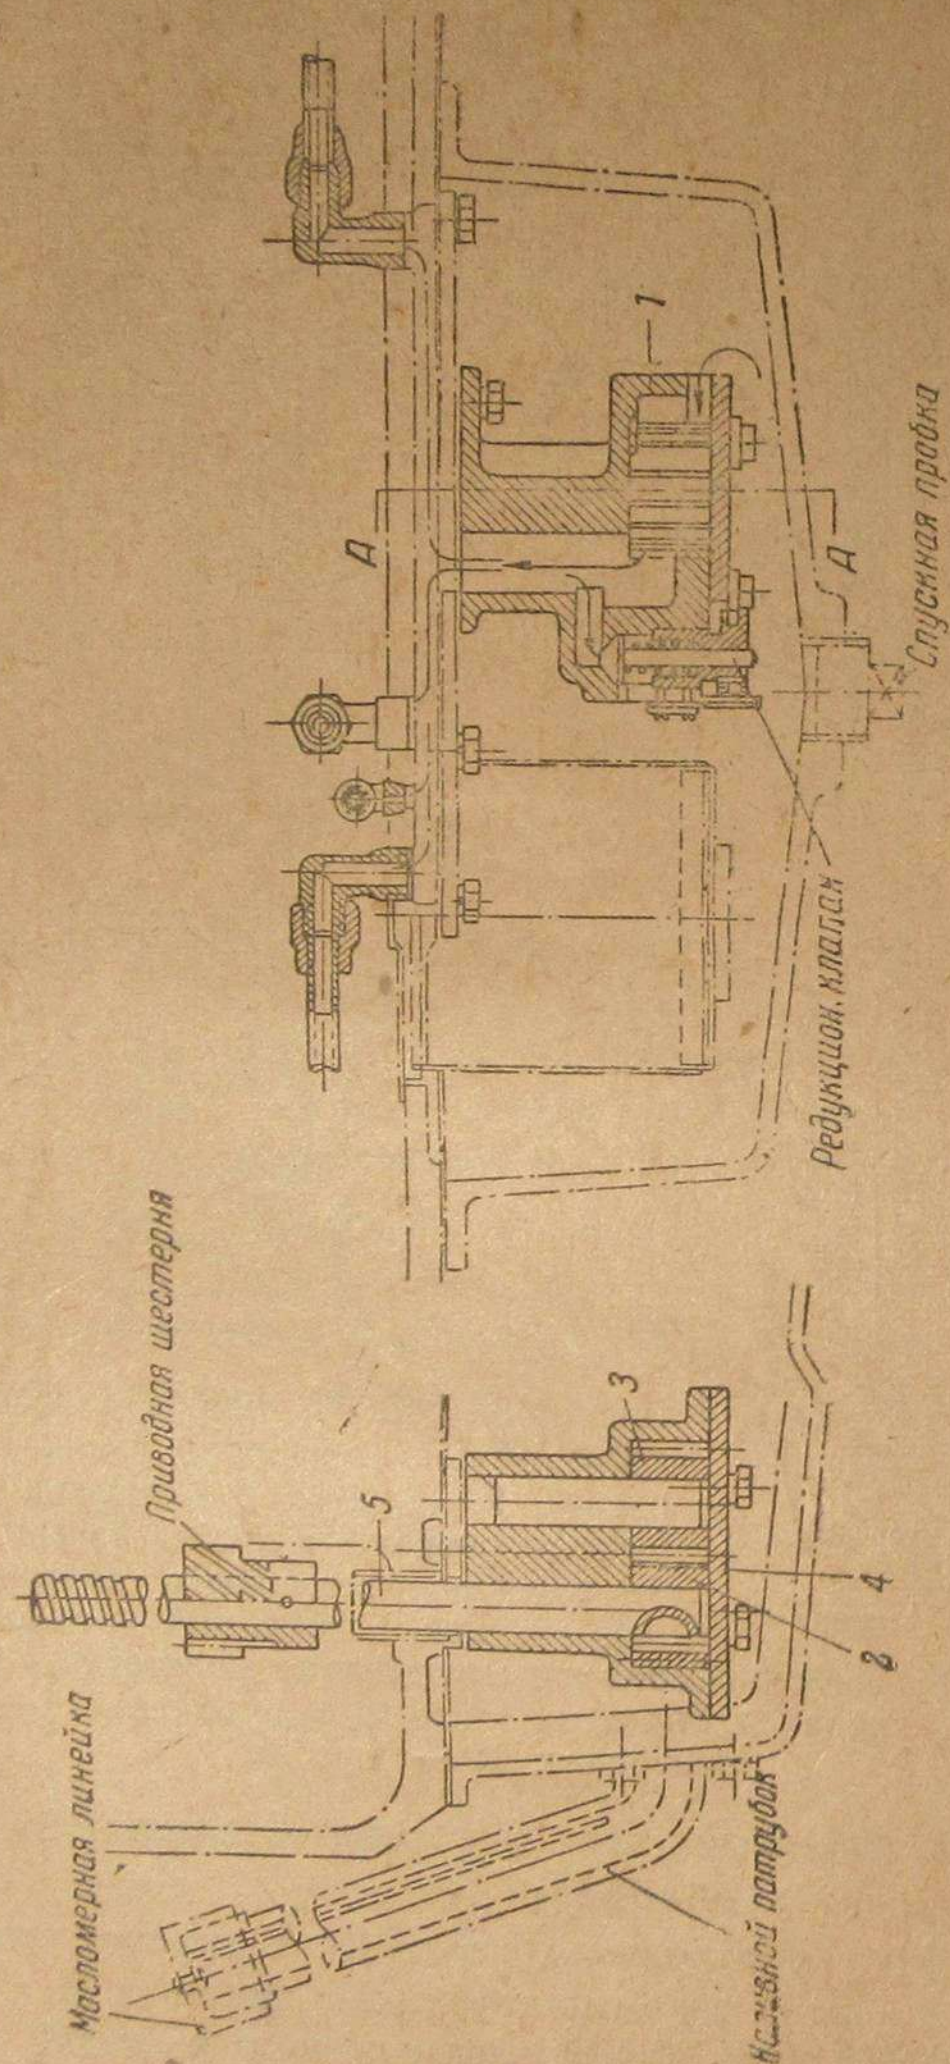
Масляный насос двигателя ЧТЗ «Сталинец-60»
